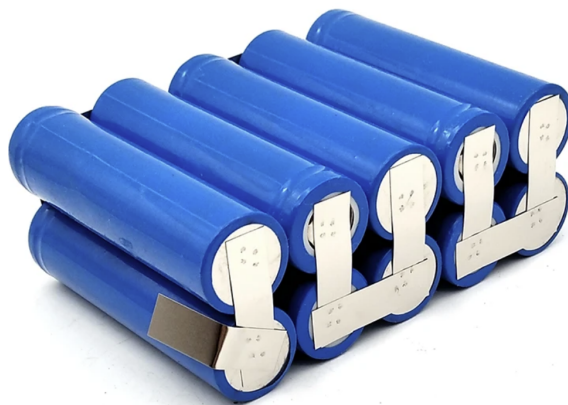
Celdas 18650 soldadas entre sí
